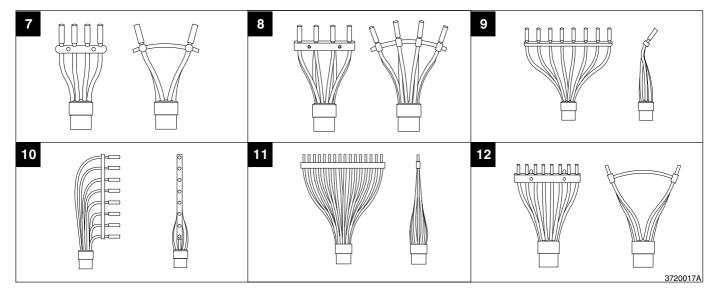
Sprühköpfe (Zeichnungen nicht maßstabsgetreu)
